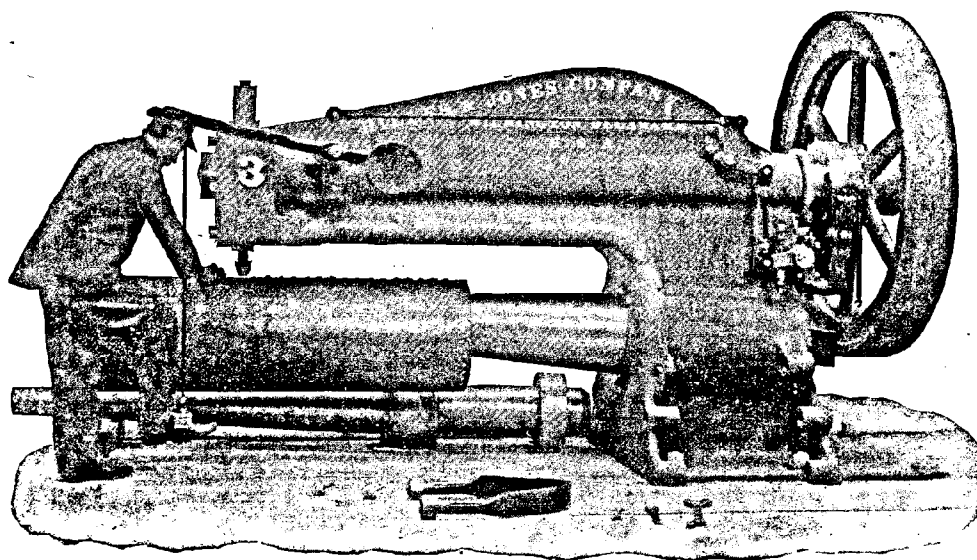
Machine à river de la Hilles et Jones Company.
